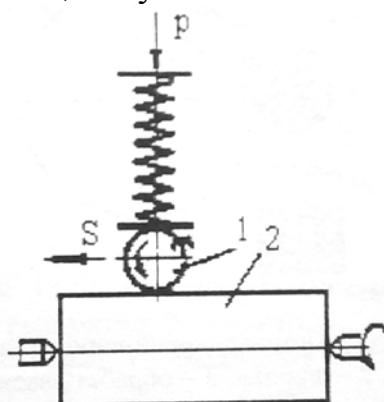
Схема упрочняюще-чистовой обработки путем обкатывания шаром (роликом)
